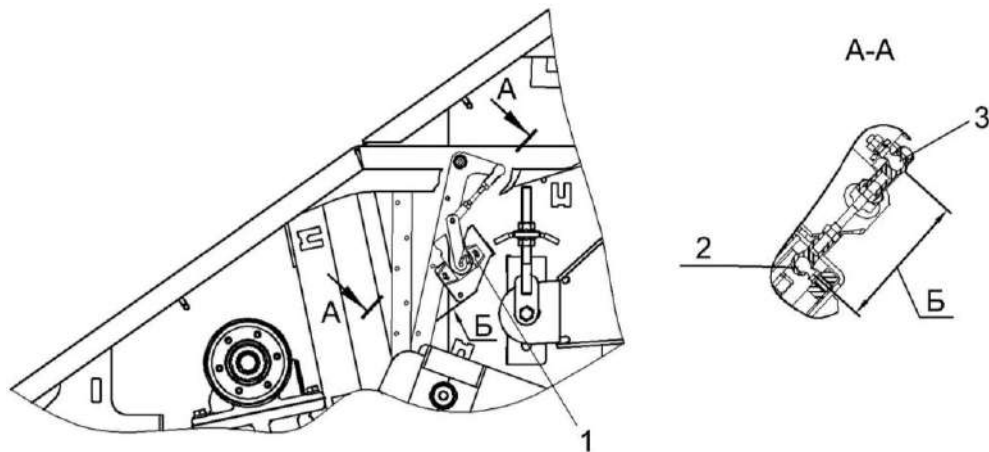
Регулировка датчика подъема мотовила (вил справа)
